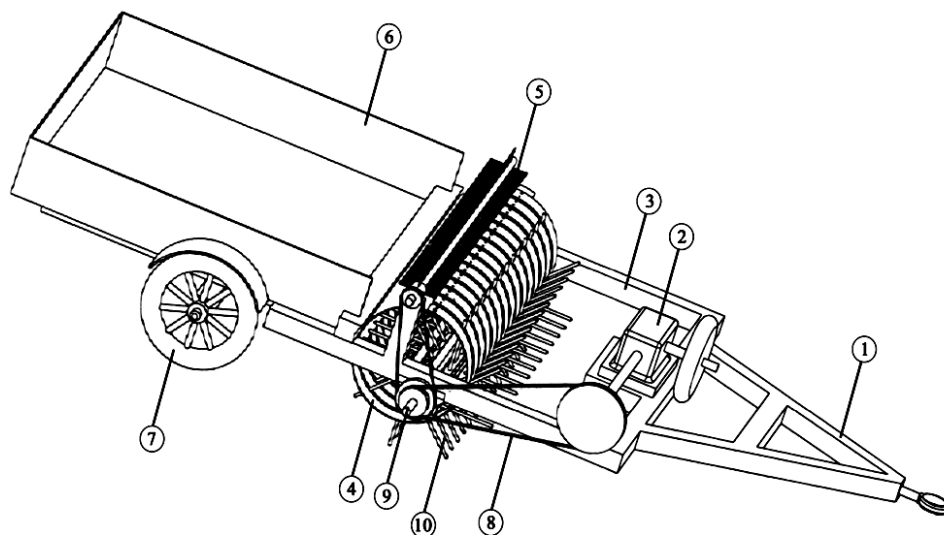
Общий вид машины «MADADKOR»: 1 - прицепное устройство; 2 - конический редуктор; 3 - рама; 4 - барабан; 5 - загрузочное приспособление; 6 - кузов; 7 - опорные колеса; 8 - ременные передачи; 9 - трубчатый (фигурный) вал; 10 - зубья
